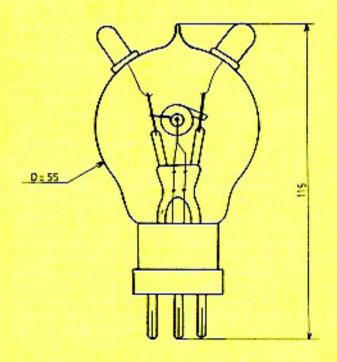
Lampe à cornes fabriquée par la S.I.F. en 1922 (brevet BEAUVAIS)
